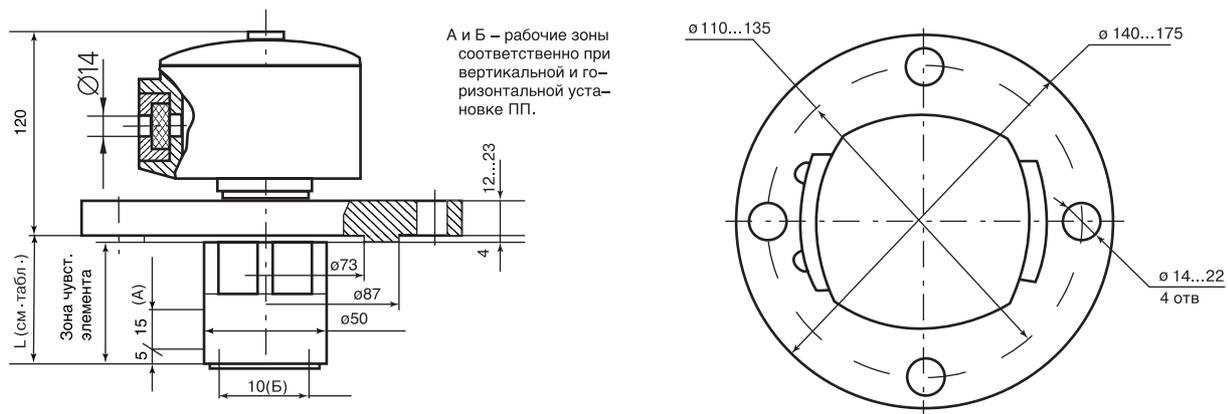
Общий вид, габаритные и установочные размеры СУС 171Р(Б)
